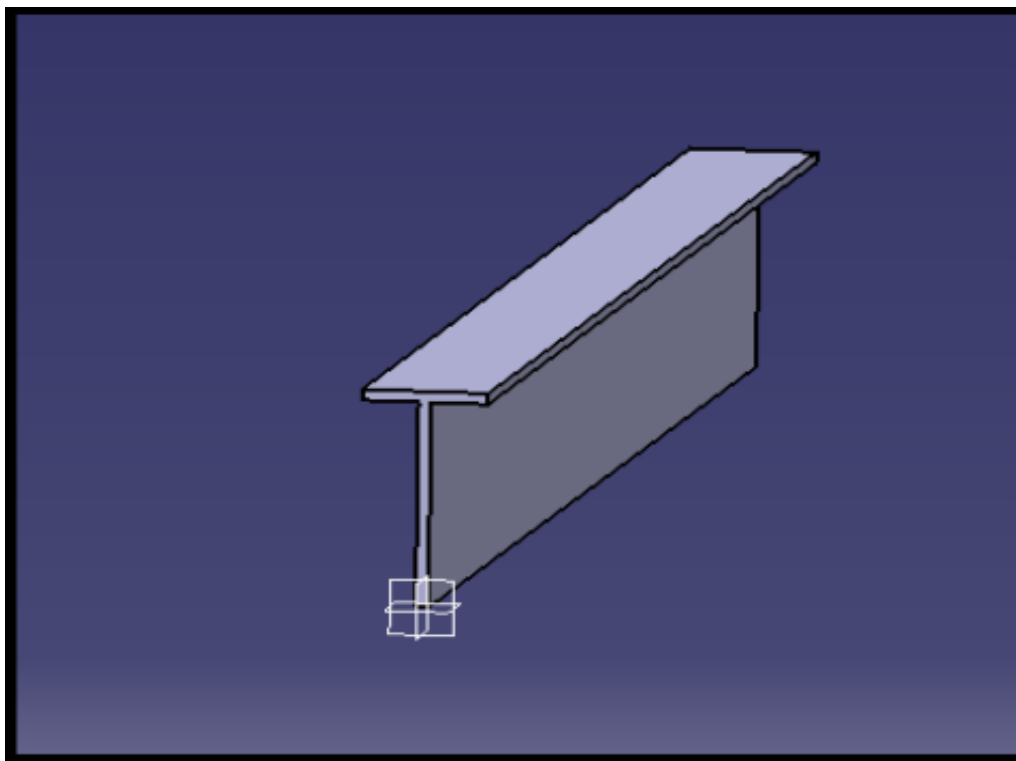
Modelagem tridimensional do perfil estrutural em seção "T" (T-Section).
